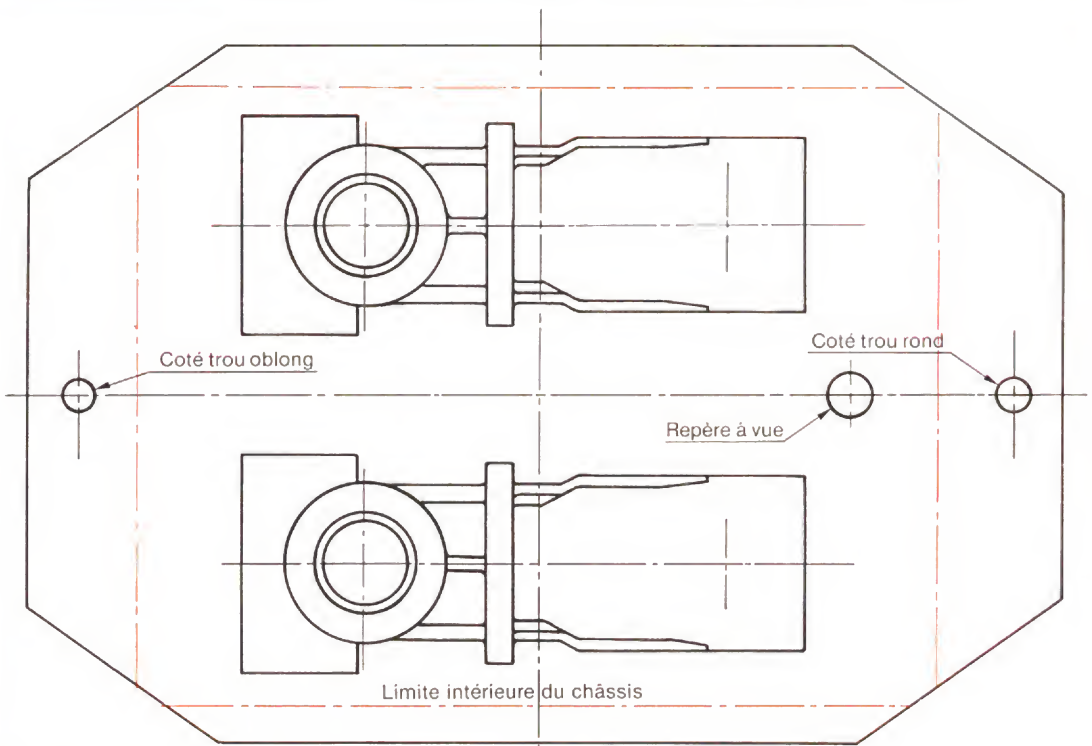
Plaque modèle pour châssis de dessous.
